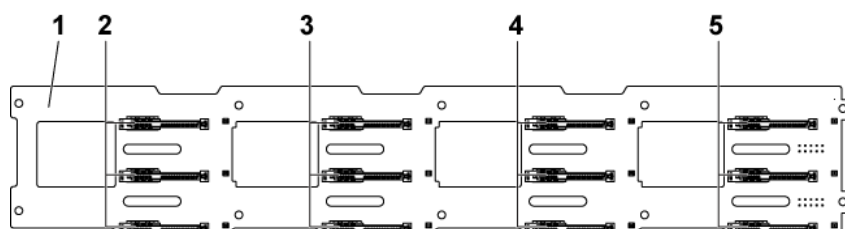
Vue frontale du fond de panier de disque dur de 3,5 pouces
